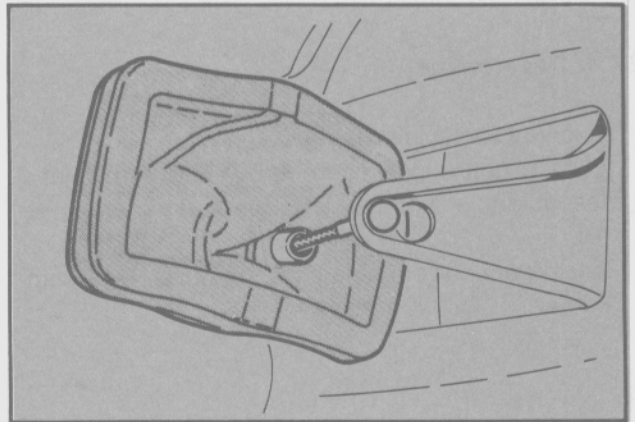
Desmontaje del guardapolvo de la horquilla de desembrague.
